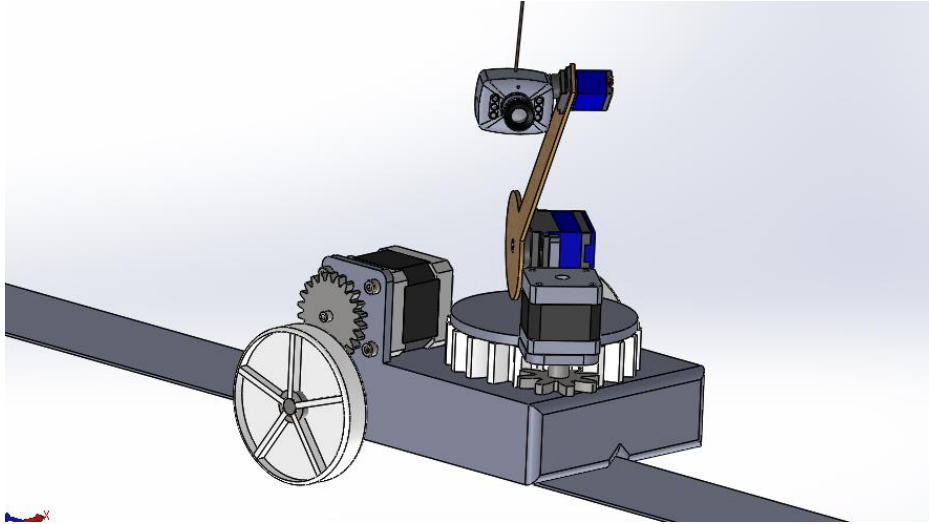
Equipo con riel guía y transmisión por engranajes [el autor]
